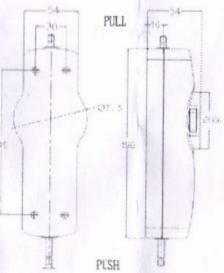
Габаритные и присоединительные размеры динамометра с цифровым отсчетным устройством ДЦ
